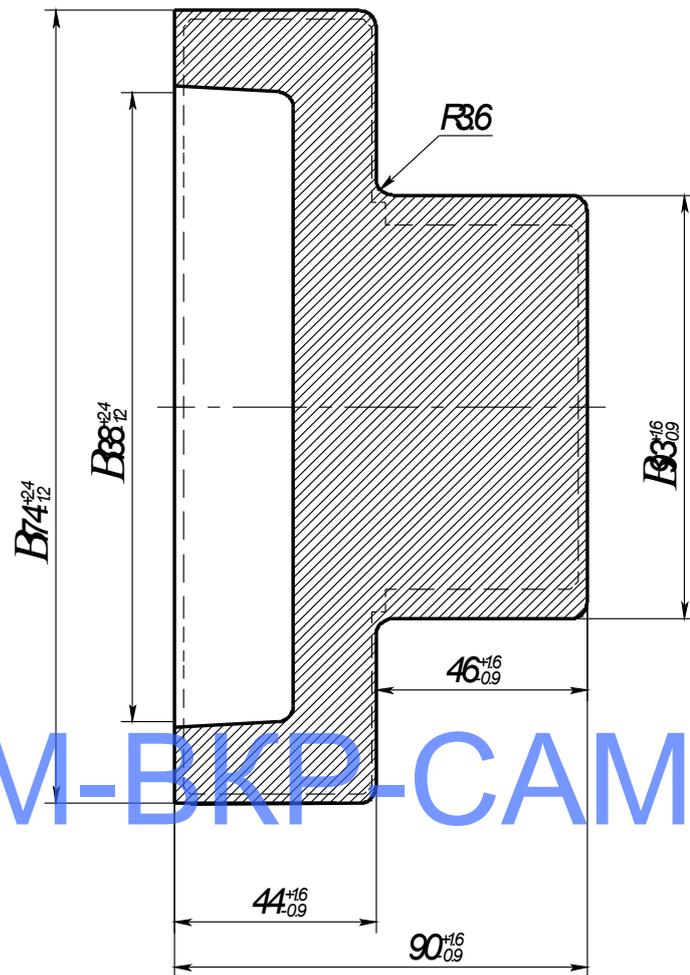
чертеж детали Полумуфта ( заготовка горячая поковка)
